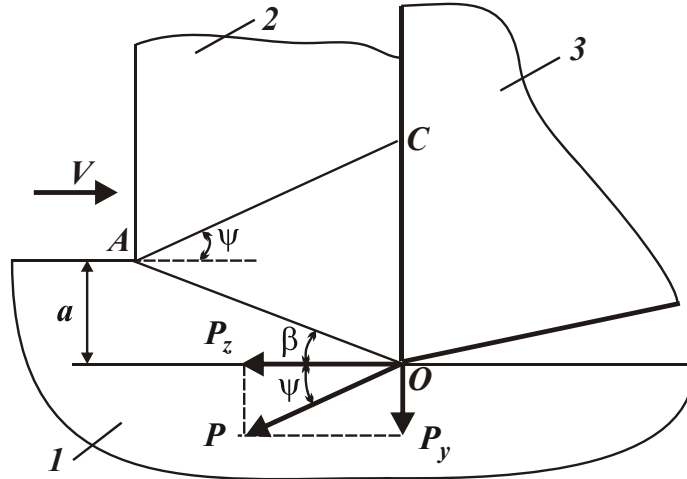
Расчетная схема параметров стружкообразования при резании: 1 – обрабатываемый материал; 2 – образующаяся стружка; 3 – режущий инструмент.
